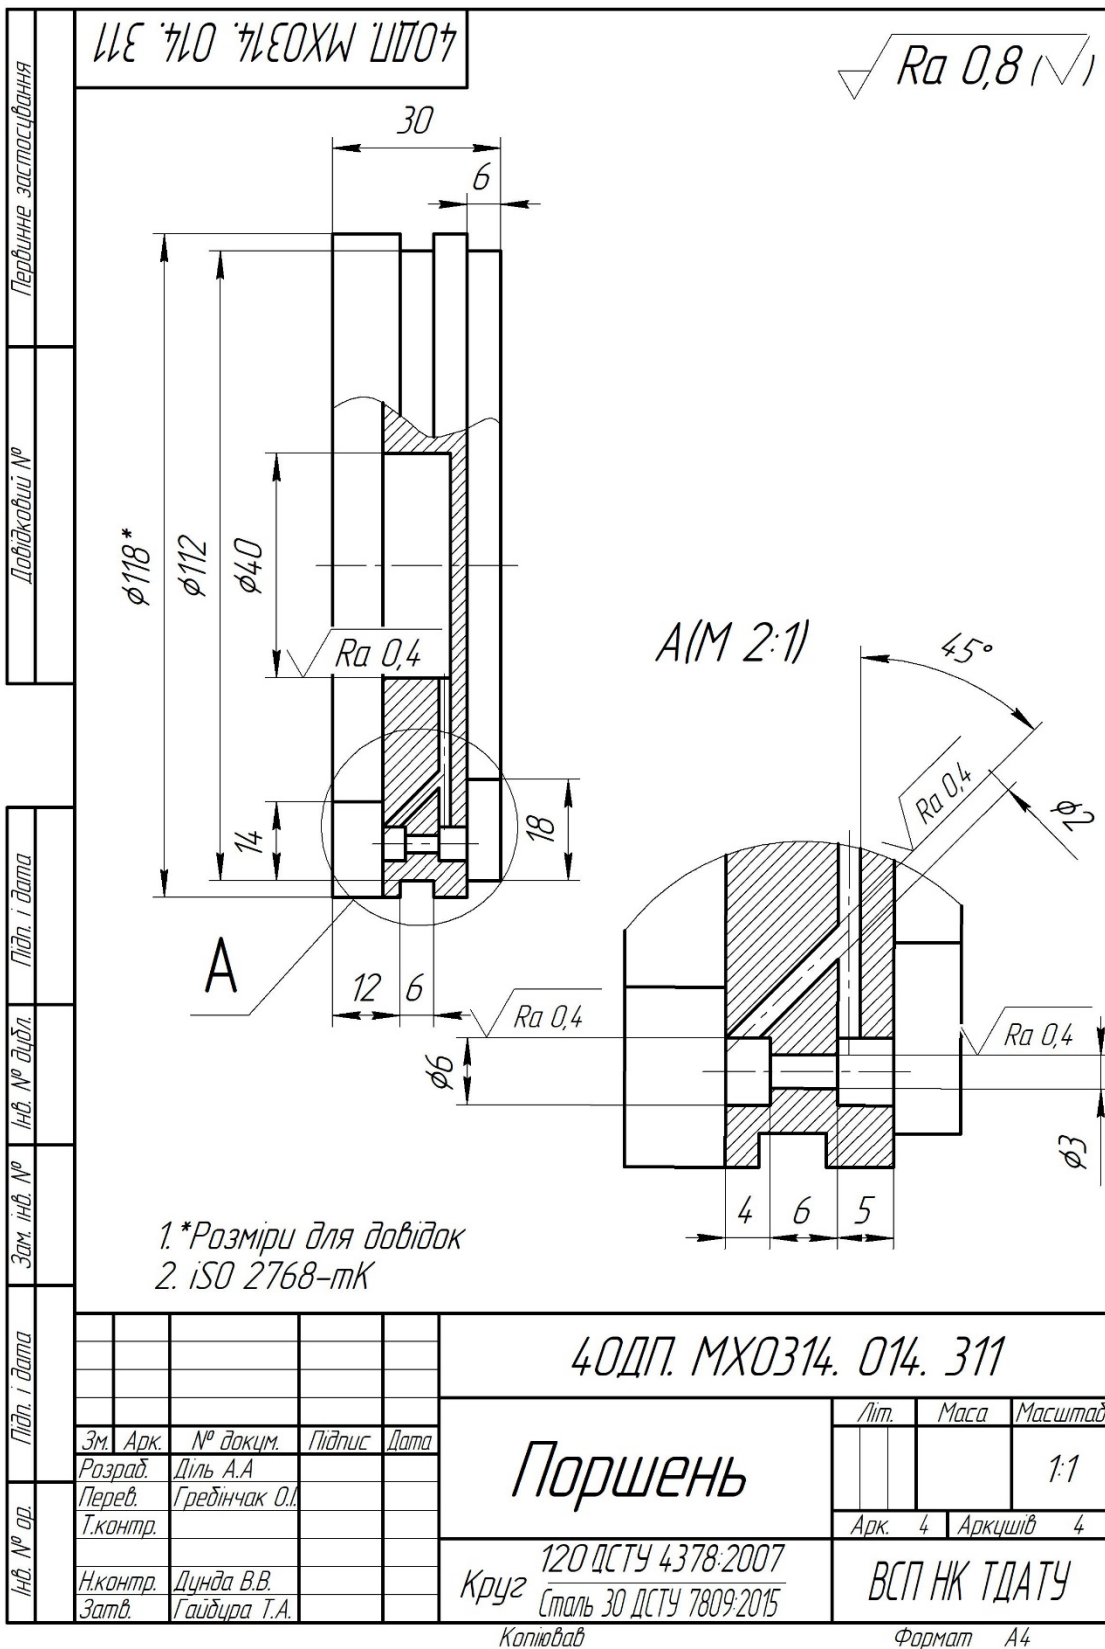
Приклад оформлення робочого кресленника деталі
